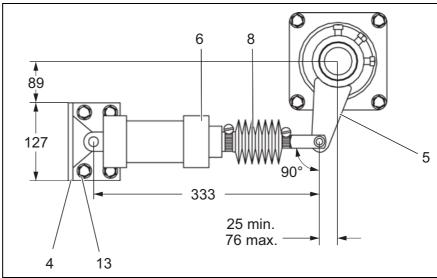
Dispositif de tension pneumatique avec vérin - dimensions d'installation
